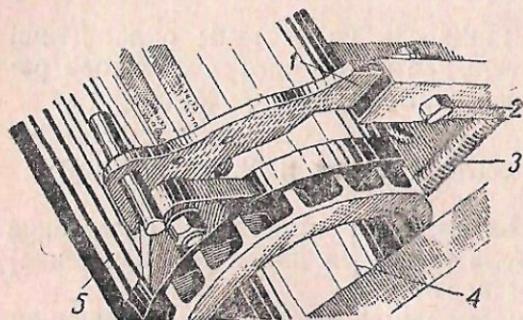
Устройство для регулировки натяжения ремня вентилятора:
